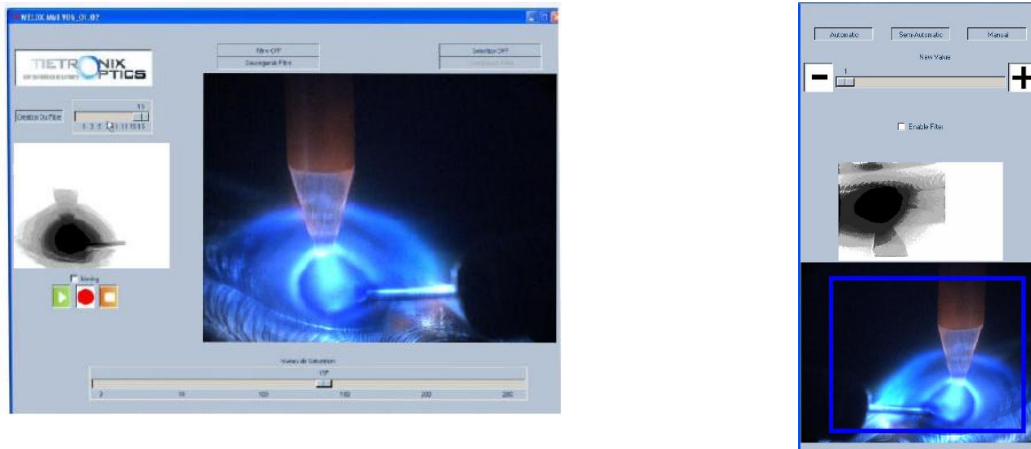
WeldX System Sistema de visión para seguimiento del charco de soldadura de manera remota. (www.tietronix-optics.com, 2009)
